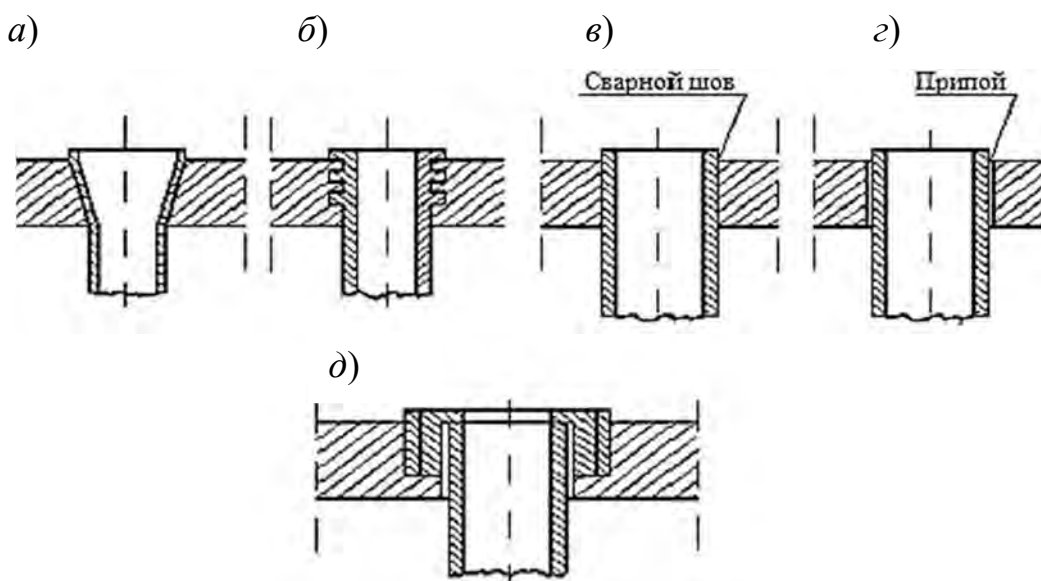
Закрепление труб в трубных решетках: *а* – развальцовкой; *б* – развальцовкой с канавками; *в* – сваркой; *г* – пайкой; *д* – сальниковыми устройствами
